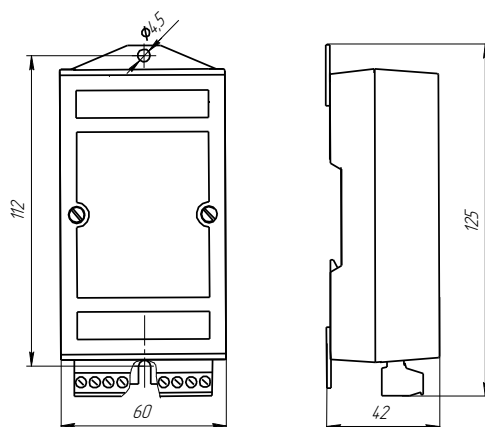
Габаритные и присоединительные размеры ПИ
